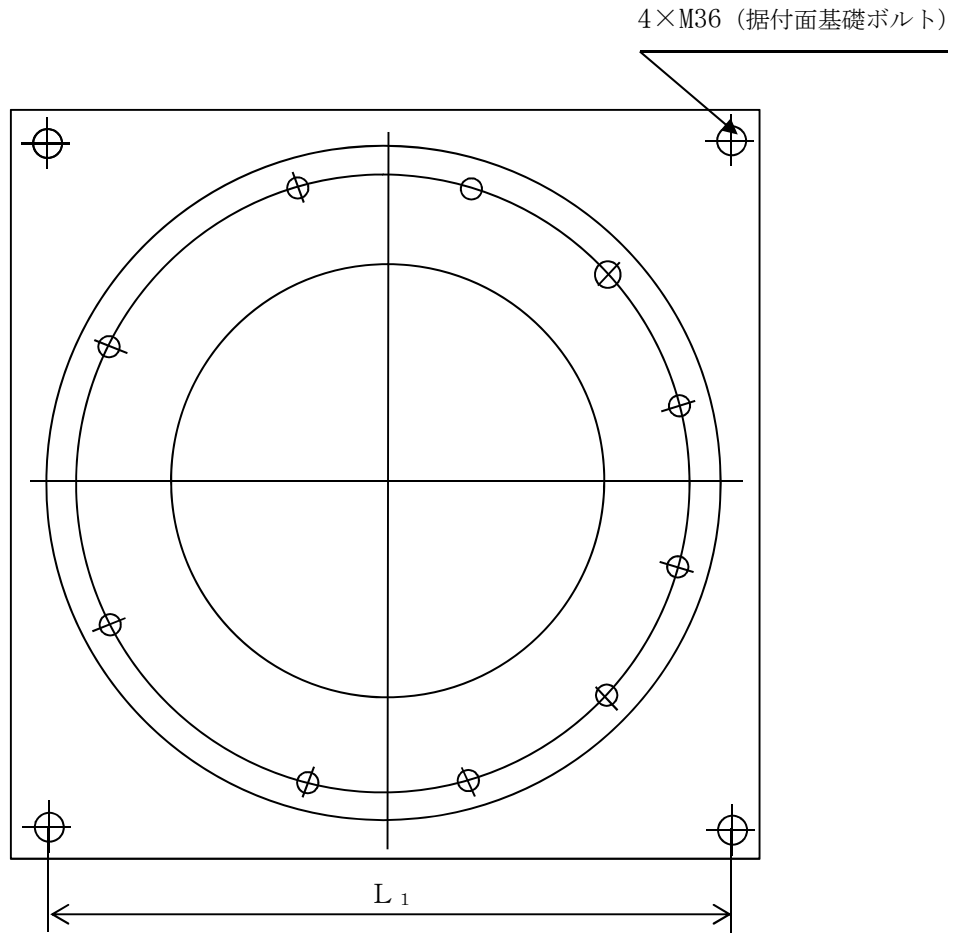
据付面基礎ボルト*の各ボルト間寸法の配置図
